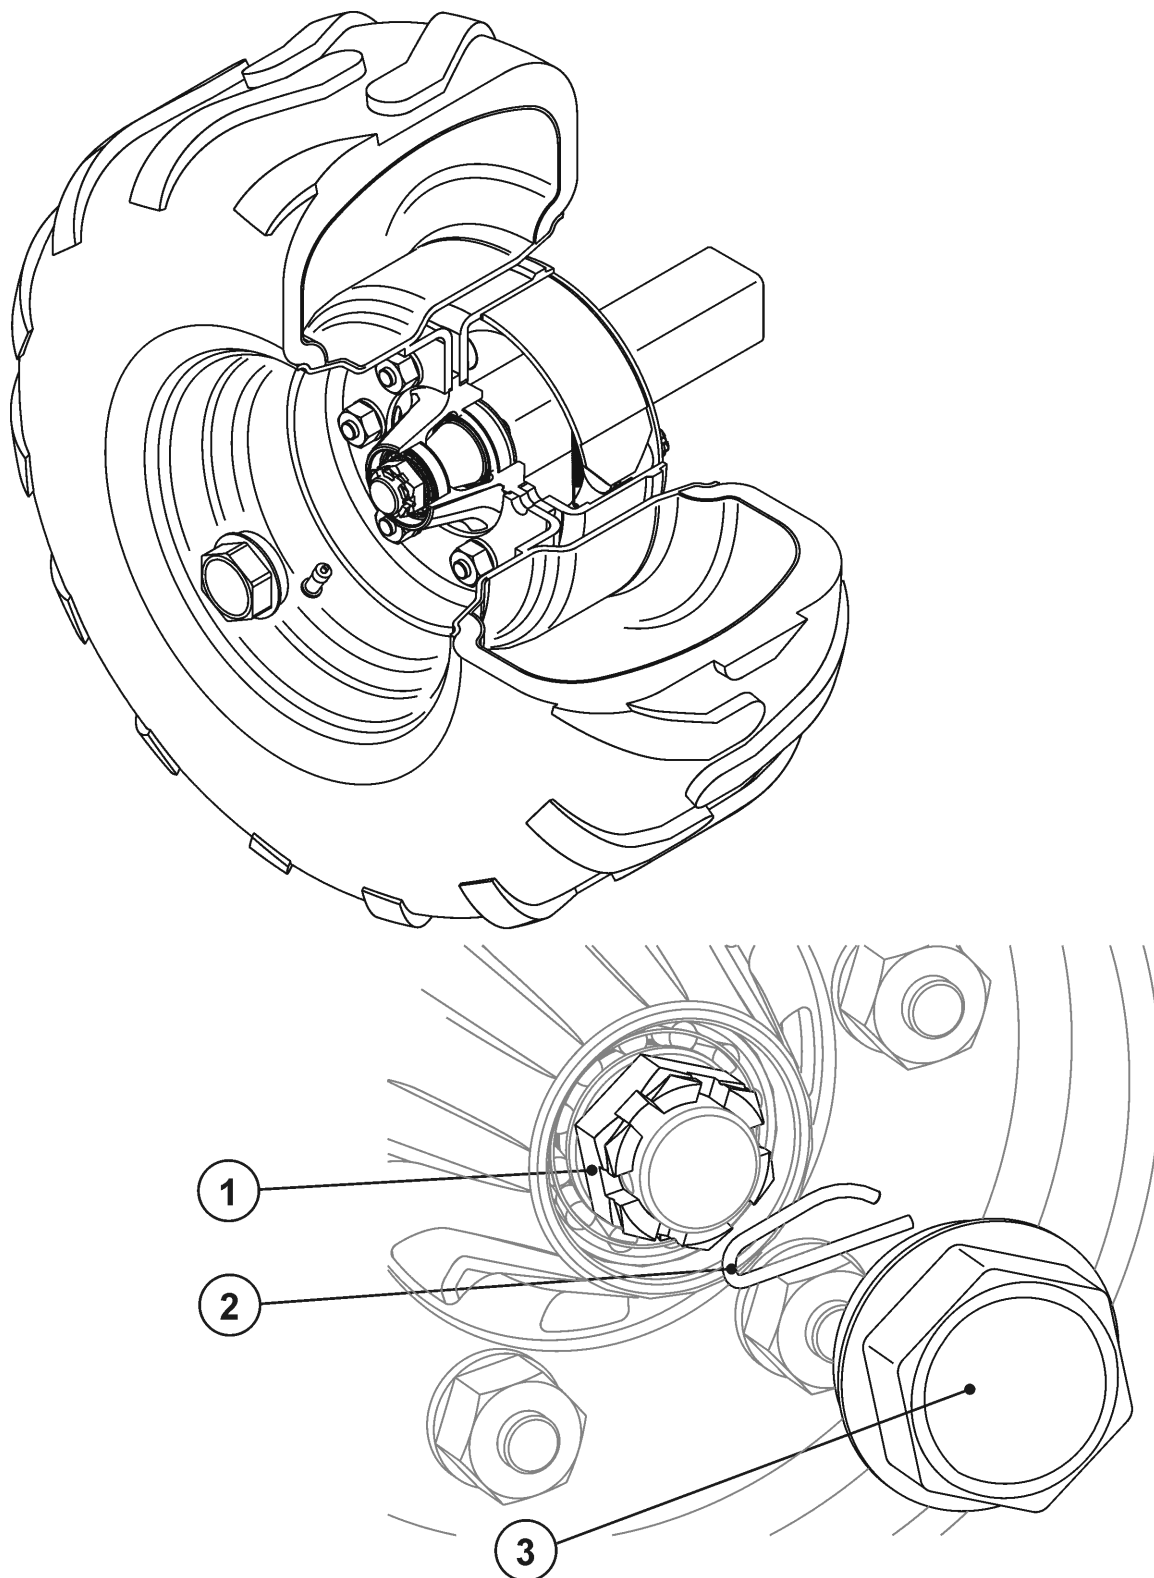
ADJUSTMENT OF WHEEL BEARINGS REGULACJA ŁOŻYSK KÓŁ JEZDNYCH
